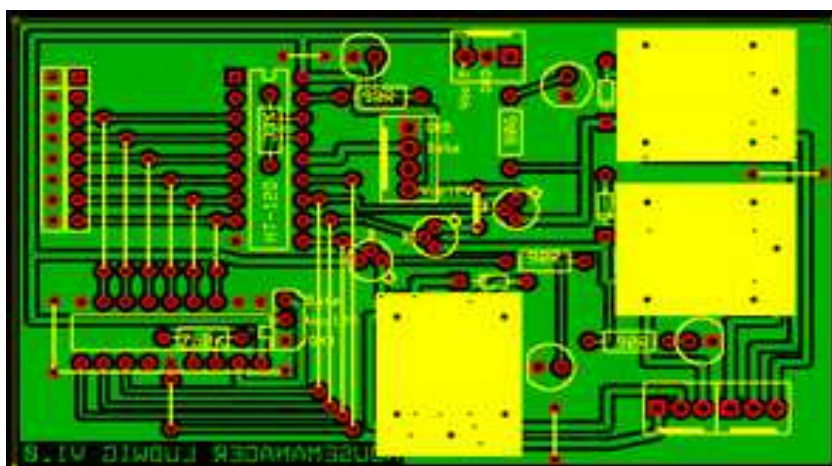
PCB - Escravo para 3 dispositivos simultâneos
